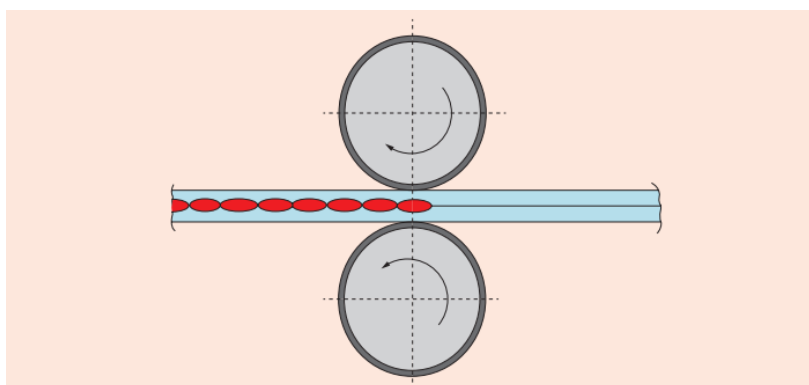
Representação esquemática da soldadura por roletes (Retirado de: Silva, 2016)
